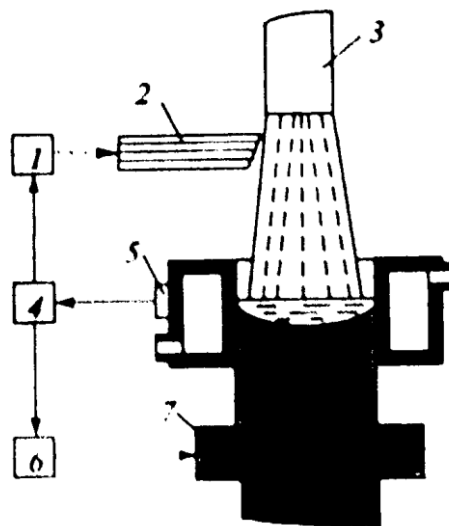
Автоматична система регулювання рівня металу в кристалізаторі при ЕПП: 1 – механізм подачі заготовки; 2 – заготовка; 3 – ЕПП, 4 – регулятор рівня; 5 – датчик рівня; 6 – механізм витягування зливку [26]
